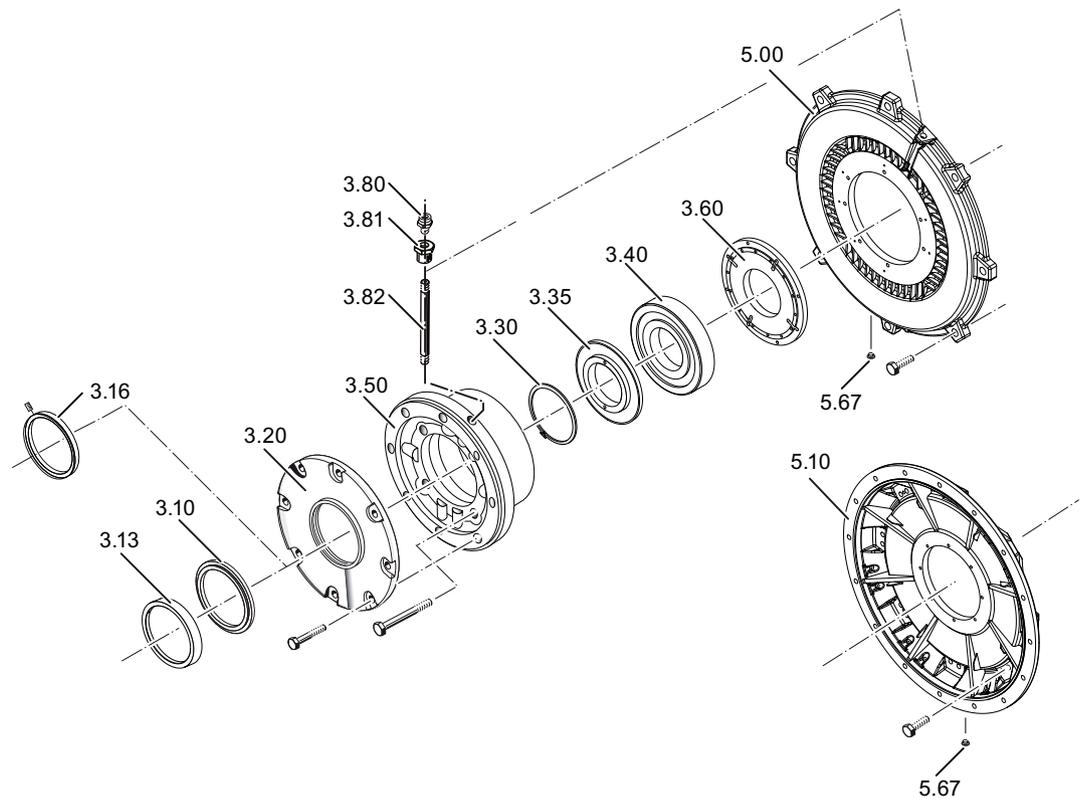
Wälzlager DE-Seite mit Lagergehäuse
